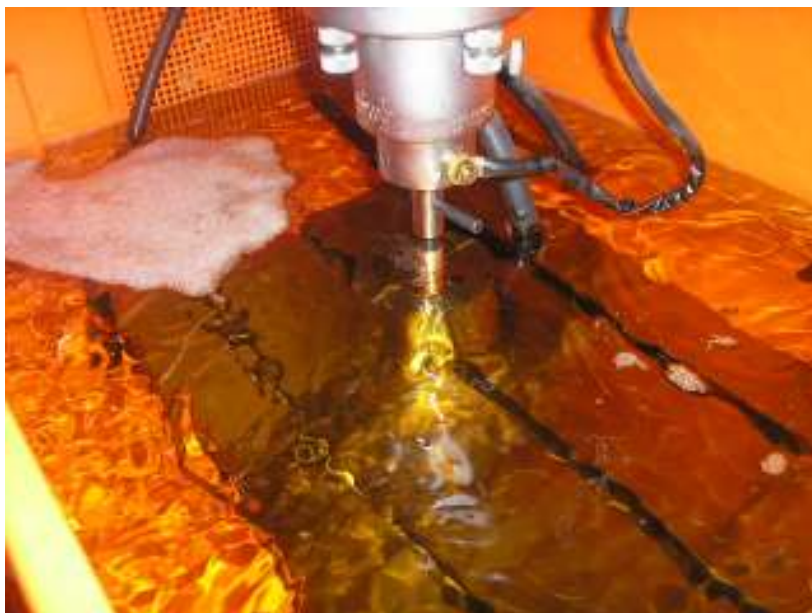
Processo de eletroerosão por penetração, realizado na Máquina Engemac 440 NC do Laboratório de Usinagem da PUC Minas.
